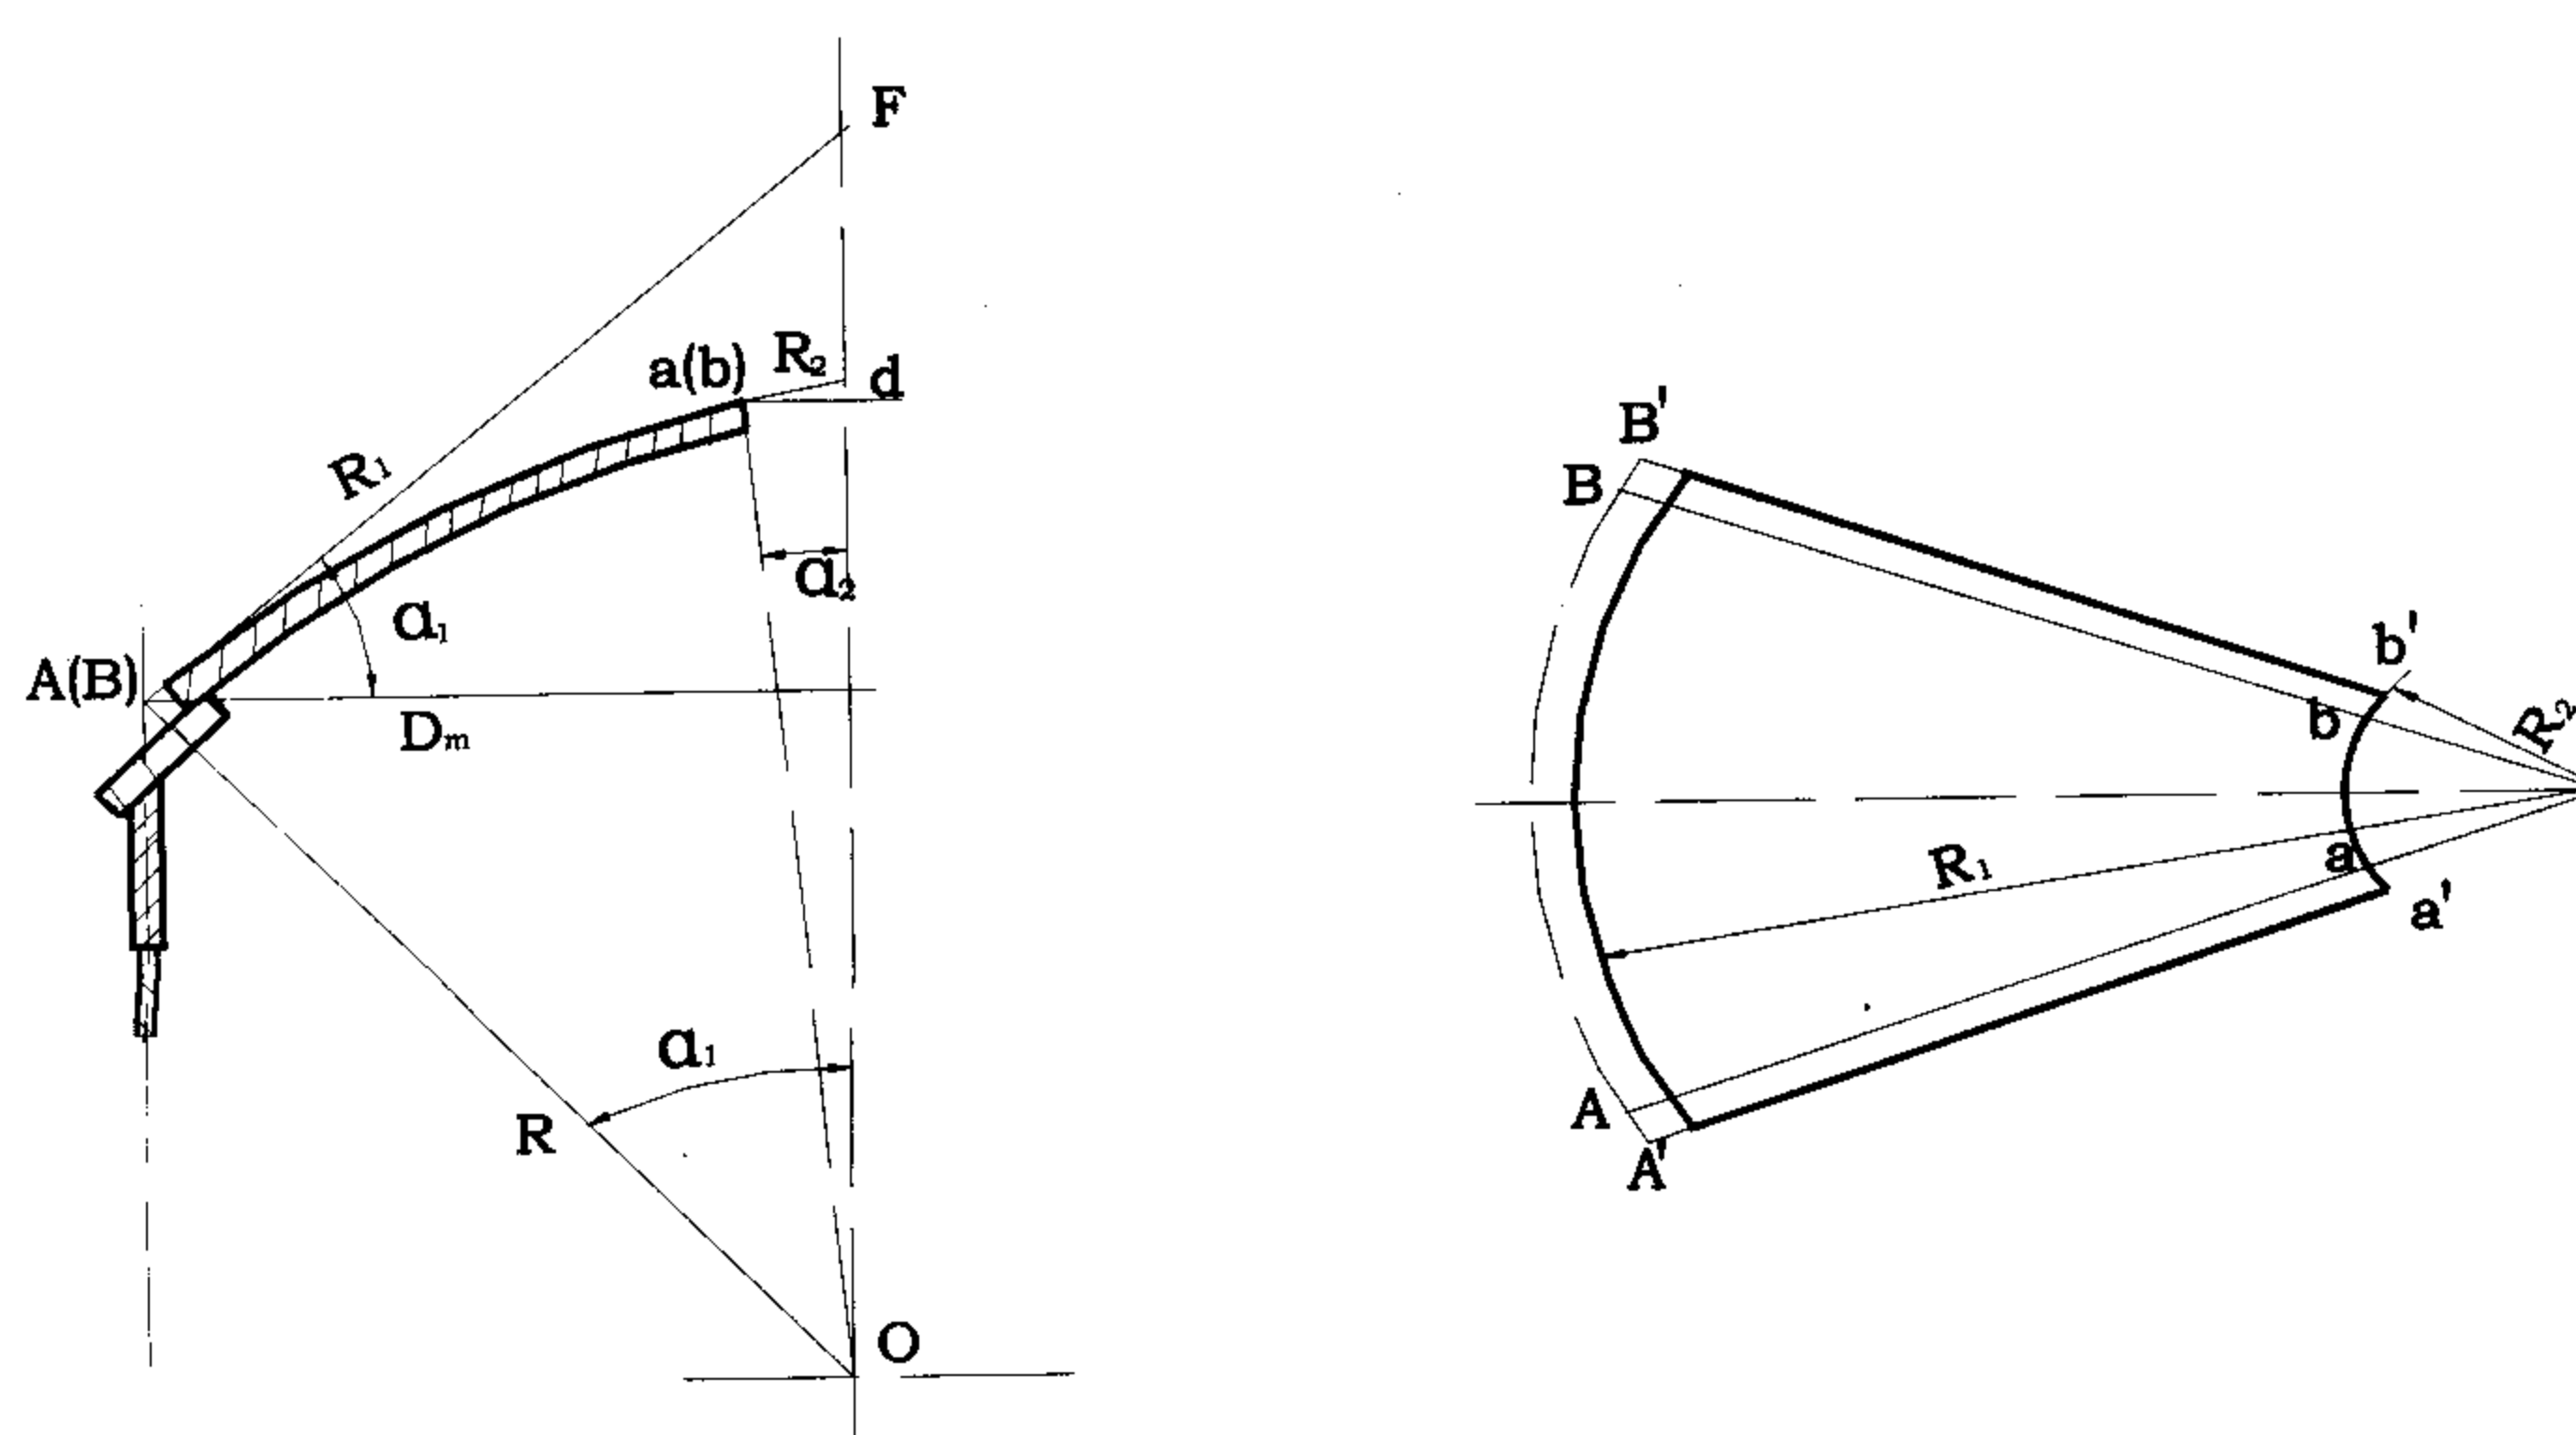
拱顶的几何尺寸及瓜瓣板尺寸
